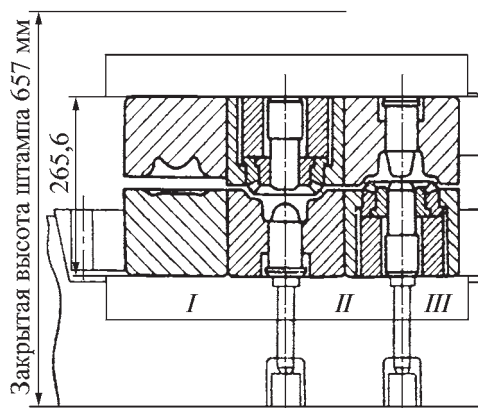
Схема штамповки шестерни с оформлением зубьев в предварительном и окончательном переходах:
